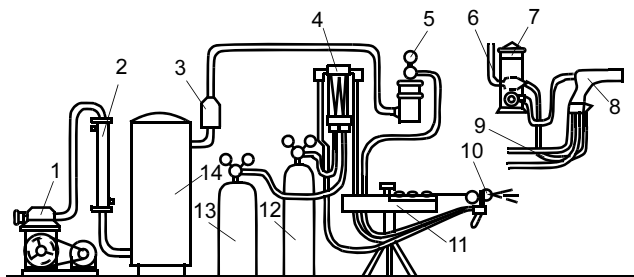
Схема установки для газопламенного напыления проволочного и порошкового материалов: 1 — компрессор; 2 — теплообменник; 3 — осушитель; 4 — расходомер; 5 — регулятор для регулирования подачи сжатого воздуха; 6 — подвод к регулятору подачи сжатого воздуха; 7 — бункер для порошка; 8 — горелка, напыляющая порошок; 9 — шланг к расходомеру; 10 — горелка, распыляющая проволоку; 11 — бухта проволоки; 12, 13 — кислородный и ацетиленовый баллоны; 14 — ресивер
